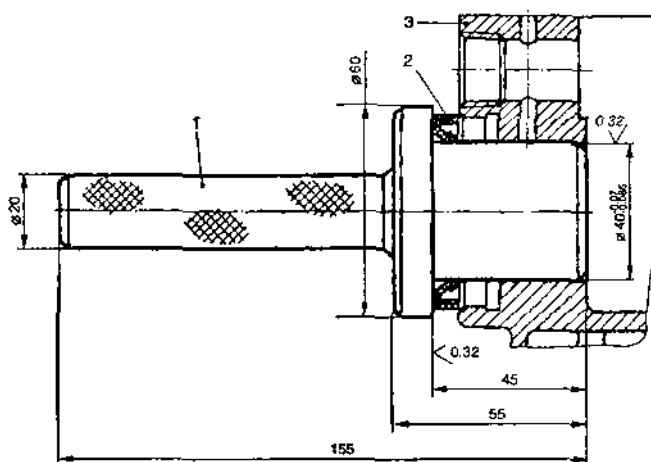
Запрессовка манжеты распределительного вала в головку цилиндров:
